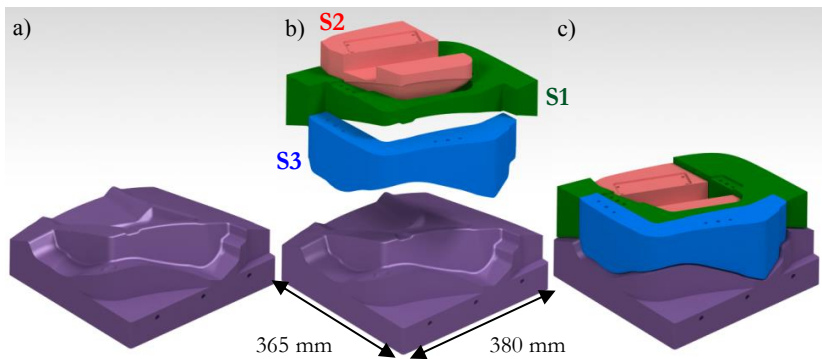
Lampentopf Demonstratorbauteil: a) Unterwerkzeug; b) Unterwerkzeug mit geöffneten Drapierstempeln (vor der Umformung); c) Unterwerkzeug mit geschlossenen Drapierstempeln (nach der Umformung).
